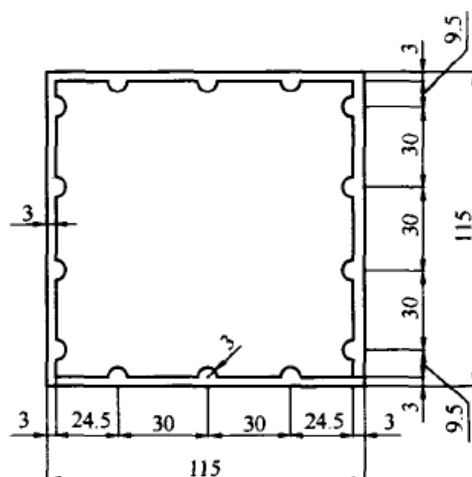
橡胶试件盒横截面示意图 (mm)
